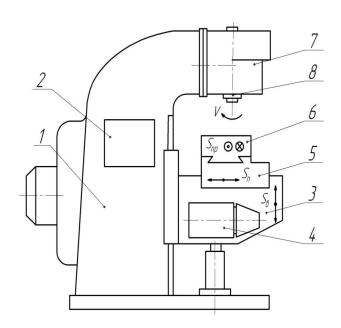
Общий вид вертикально-фрезерного станка
